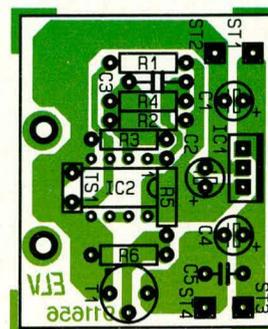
Bestückungsplan der Steuerung. TS 1 wird über Zuleitungen angeschlossen oder seitlich abgewinkelt.
